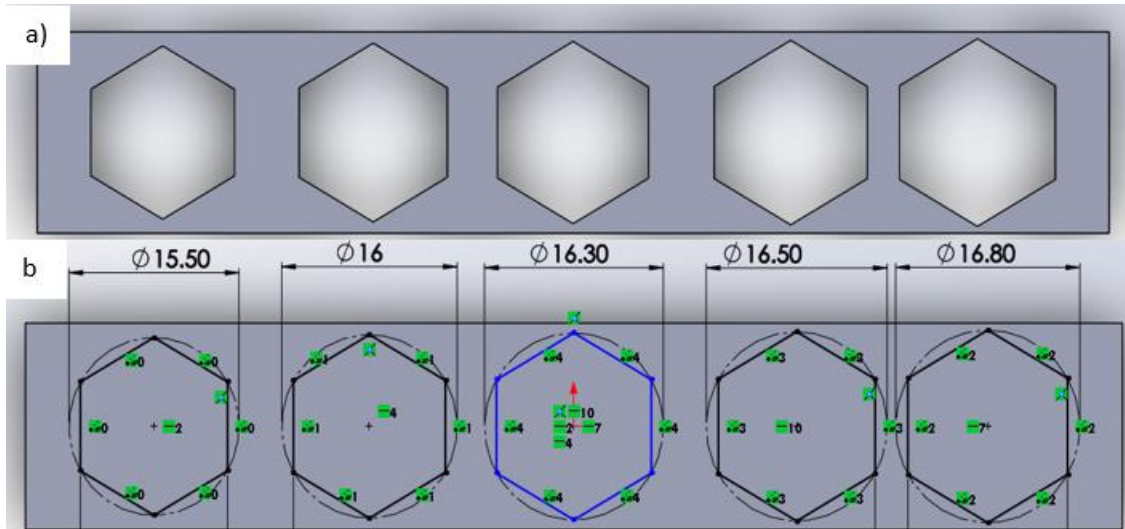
a) Pieza hembra para pruebas de tolerancia. b) Dimensiones de los barrenos.
